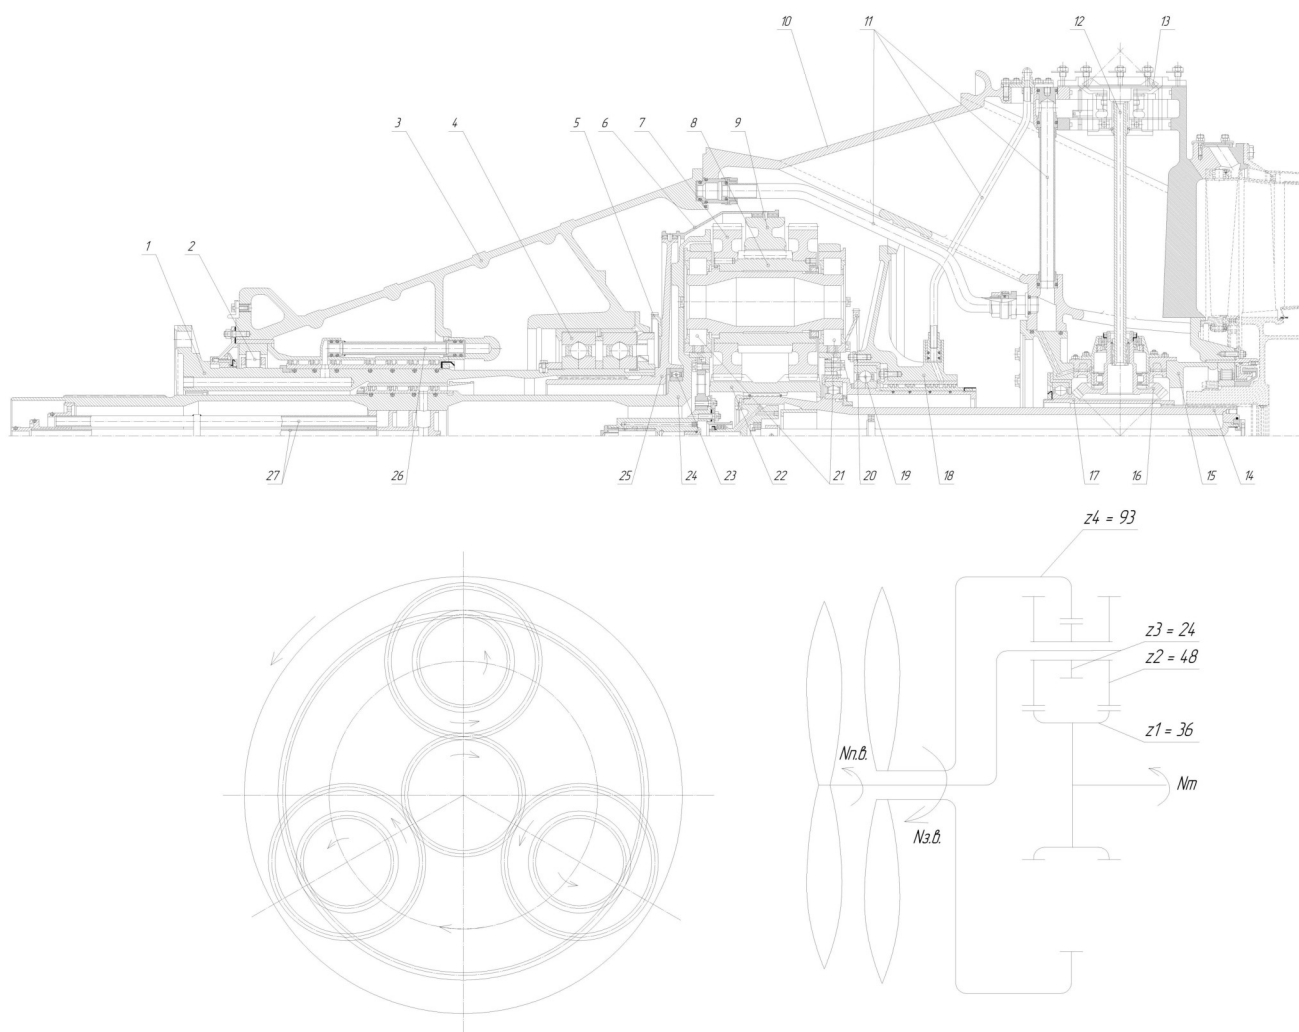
Дифференциальный редуктор ТВД НК-12МВ: 1 - вал заднего винта; 2, 21 - роликовый подшипник; 3 - картер вала заднего винта; 4 19, 23 - шариковые подшипники; 5 - шестерня привода регулятора заднего винта; 6 - муфта; 7 - сателлитные шестерни; 8 - шестерня-вал; 9 - центральная наружная шестерня; 10 - картер редуктора; 11 - трубы; 12 - приводной валик; 13 - коническая шестерня; 14 - приводной вал; 15 - корпус центрального привода; 16 - коническая шестерня привода агрегатов; 17 - центральная коническая шестерня; 18 - корпус приводов; 20 - шестерня; 22 - центральная внутренняя шестерня; 24 - вал переднего винта; 25 - соединительный диск; 26 - трубки подвода масла к маслораспределительной втулке; 27 - трубки подвода масла к переднему винту
